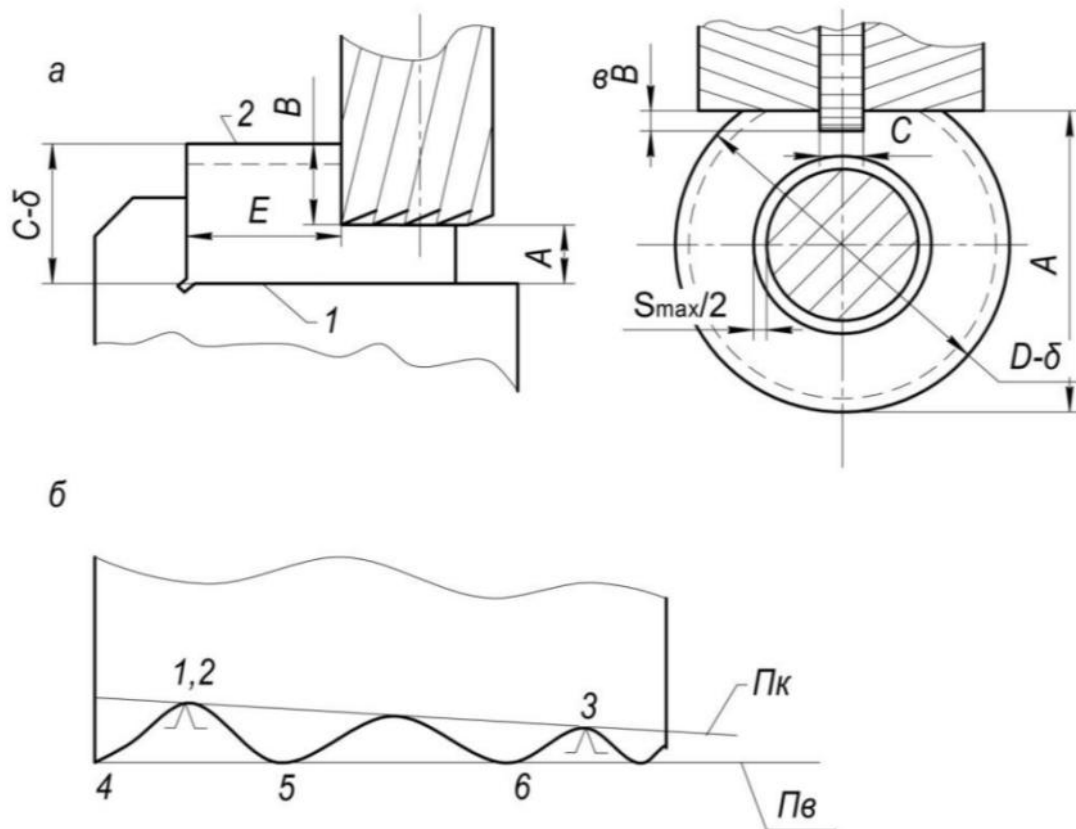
Схеми установки деталей при обробці для розрахунку похибки базування
